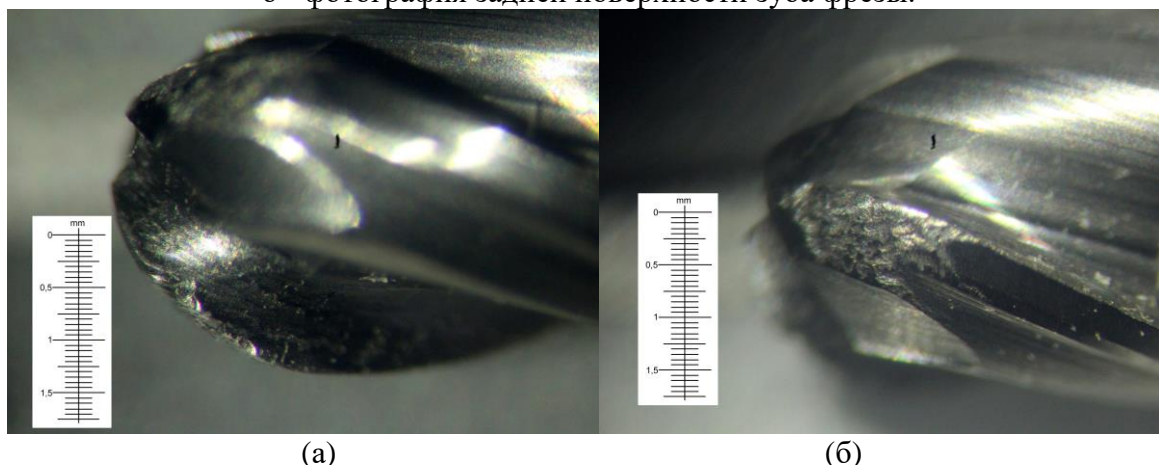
Фотография конической фрезы. а – фотография передней поверхности зуба фрезы; б - фотография задней поверхности зуба фрезы.
